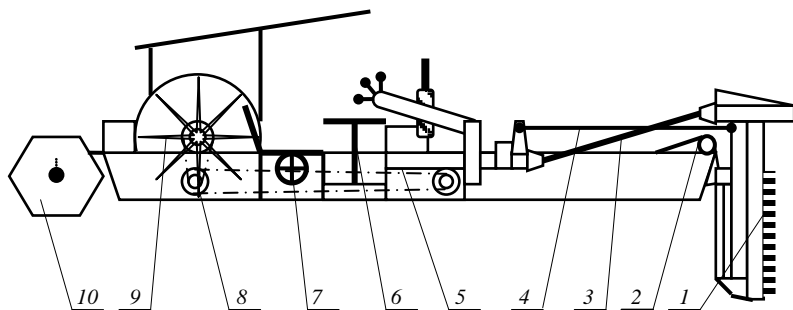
Схема лодки-косилки ЛК-12: 1 – Т-образный режущий аппарат; 2 – трос; 3 – карданная передача; 4 – рама; 5 – двигатель; 6 – рулевое колесо; 7 – лебедка; 8 – цепная передача; 9 – гребные колеса; 10 – рули
